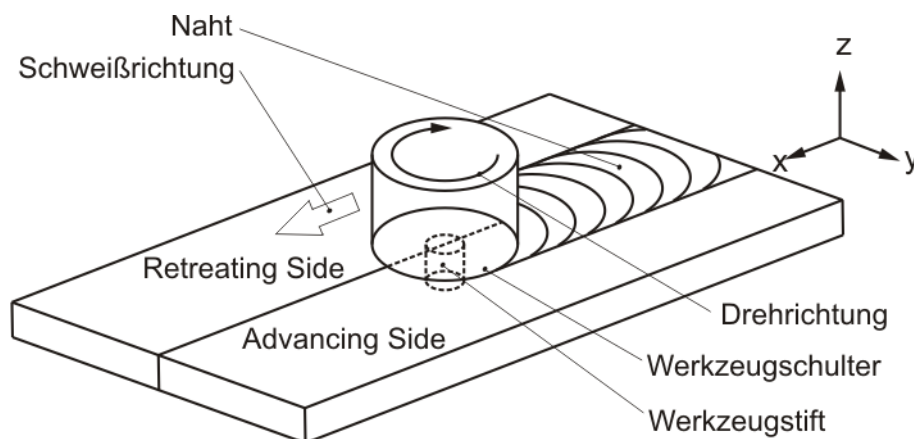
Seitendefinition beim Rührreißschweißen
